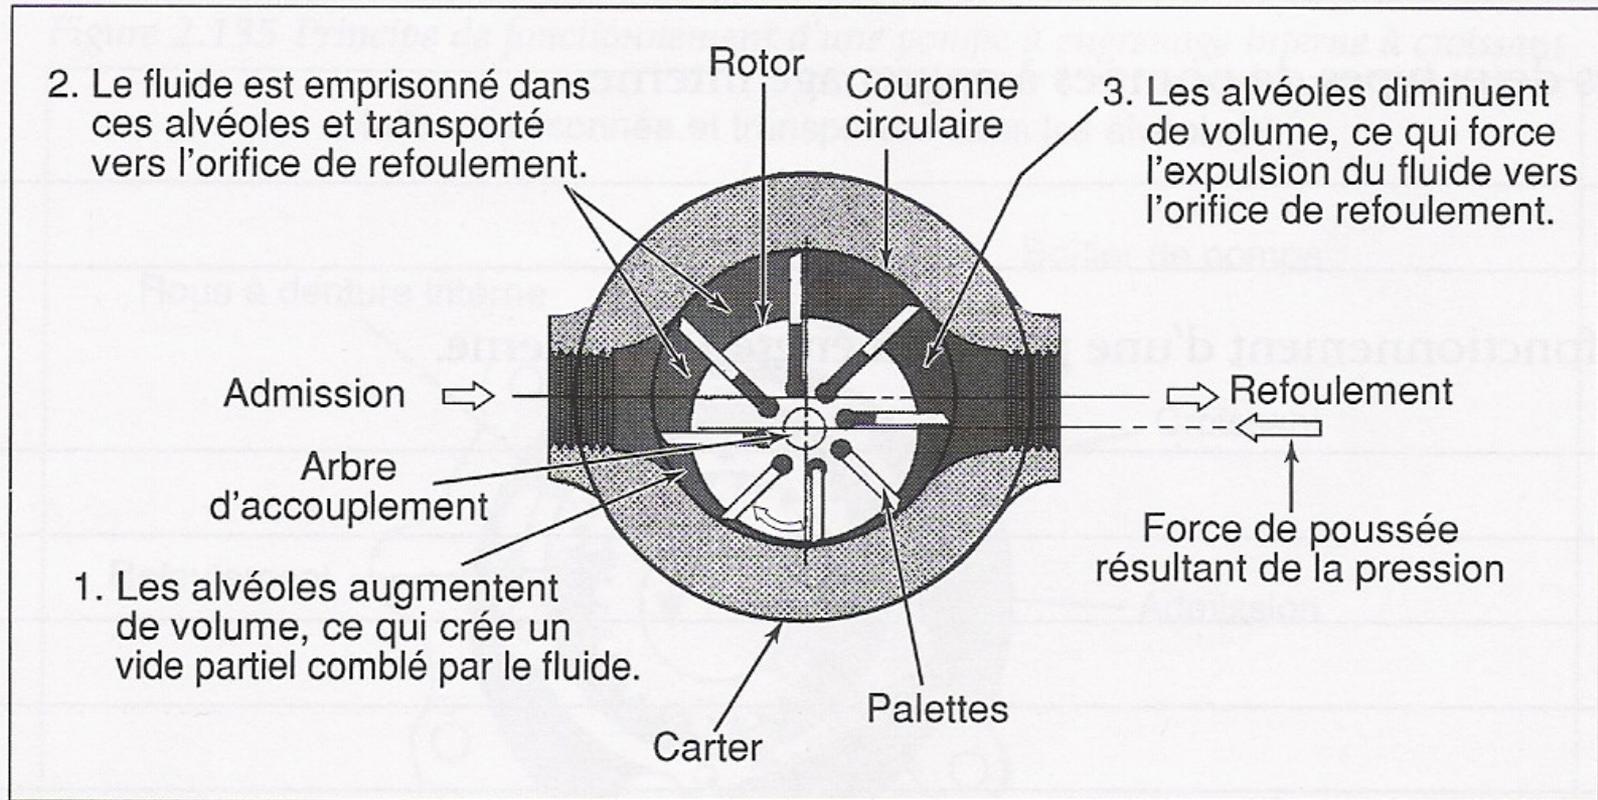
Pompe à palettes à cylindrée fixe à rotor balancé
